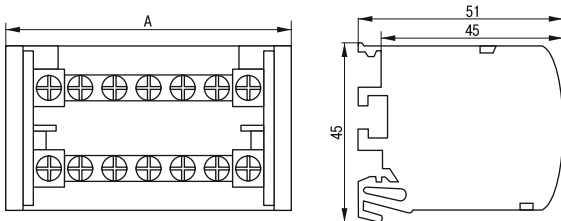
Габаритные размеры шин ШНК 2×7, ШНК 2×11 и ШНК 2×15 /
